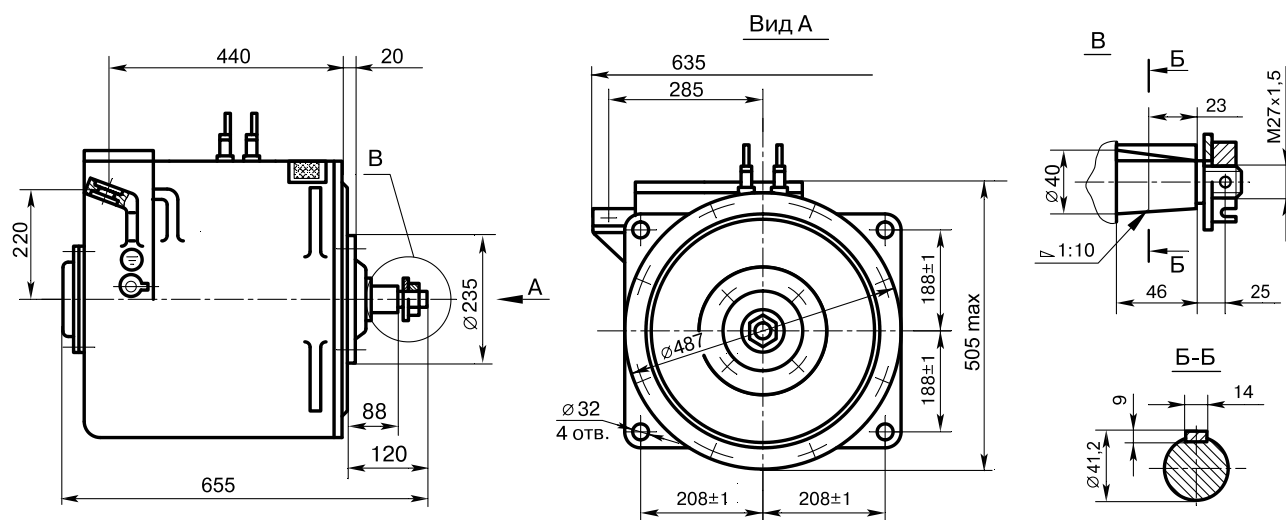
Габаритные и установочные размеры электродвигателя ДРТ-12
